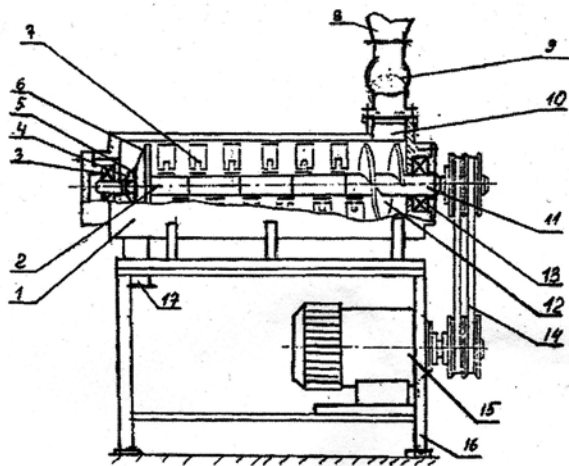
Конструкция скоростного гранулятора: 1 – корпус; 2 – втулка; 3 – подшипник; 4 – гайка; 5 – стопорная шайба; 6 – отбойный диск; 7 – плоская лопатка; 8 – загрузочный бункер; 9 – секторный питатель; 10 – загрузочный патрубок; 11 – рабочий вал; 12 – транспортирующий шнек; 13 – подшипник; 14 – клиноременная передача; 15 – электродвигатель; 16 – рама; 17 – патрубок выгрузки.
